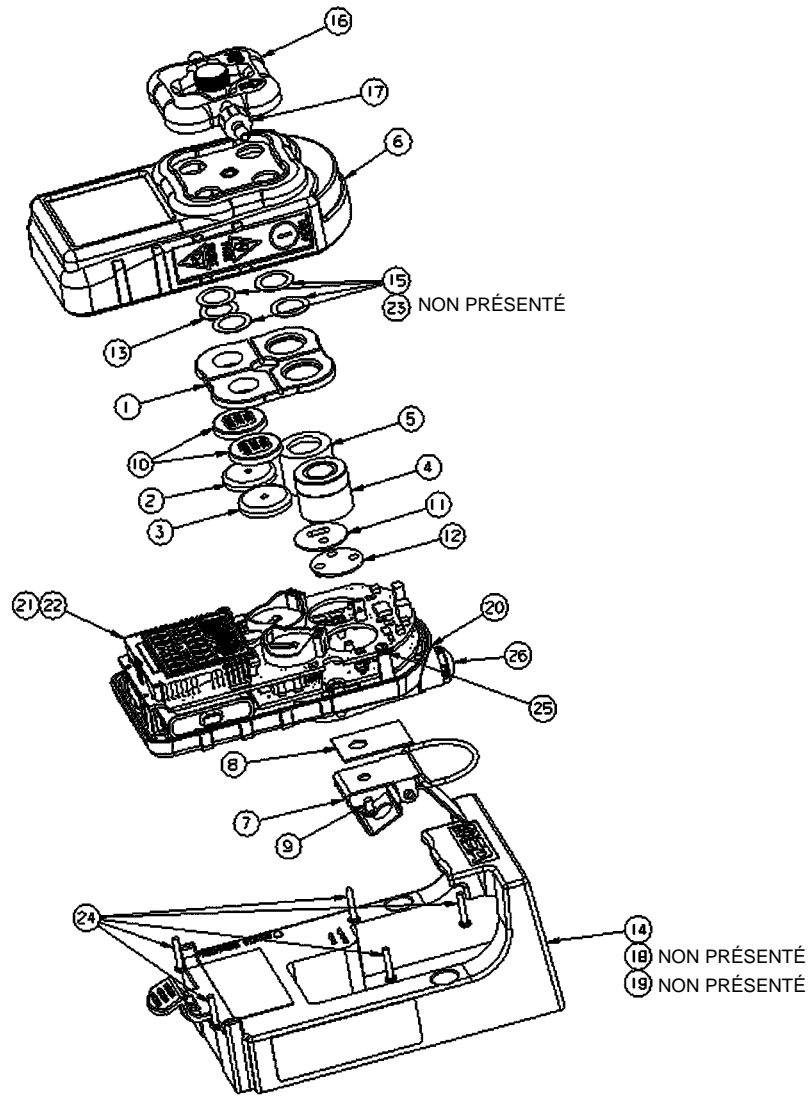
Pièces de remplacement (voir Table 7-1)
